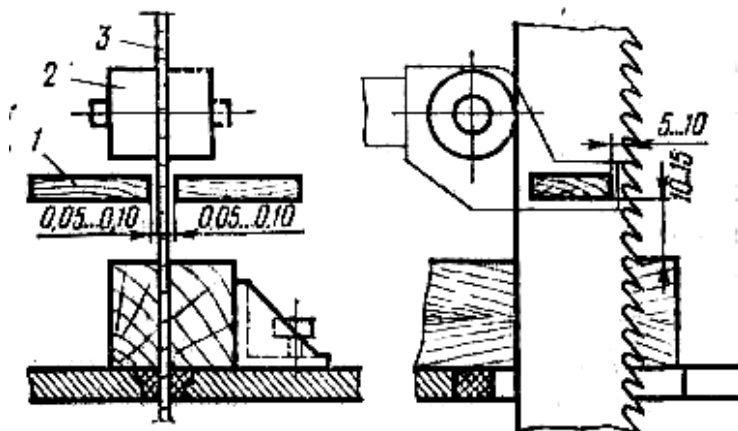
Наладка направляющего устройства для пилы ленточнопильного станка: 1 — направляющая бобышка; 2 — ролик, 3 — пила
